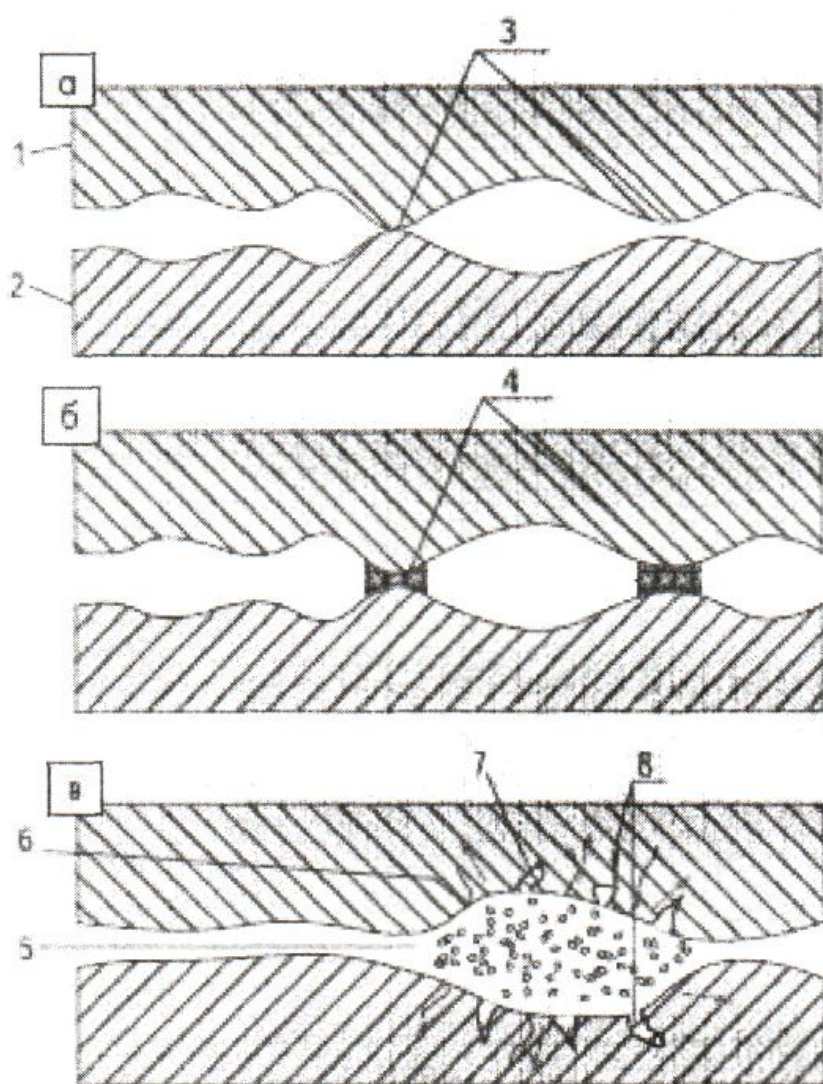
Механизм изнашивания металлических поверхностей при фреттинг-коррозии:
